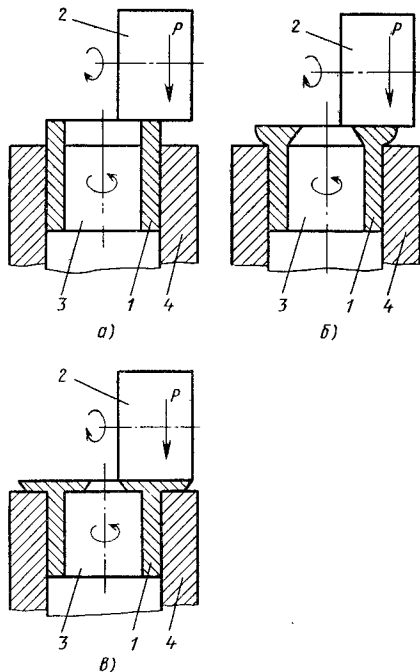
Схема холодной торцовой раскатки кольцевой детали с Т-образным буртом: а — начало процесса раскатки; б — промежуточная стадия раскатки; в — конечная стадия раскатки; 1 — заготовка; 2 — деформирующий валок; 3 — оправка; 4 — матрица
